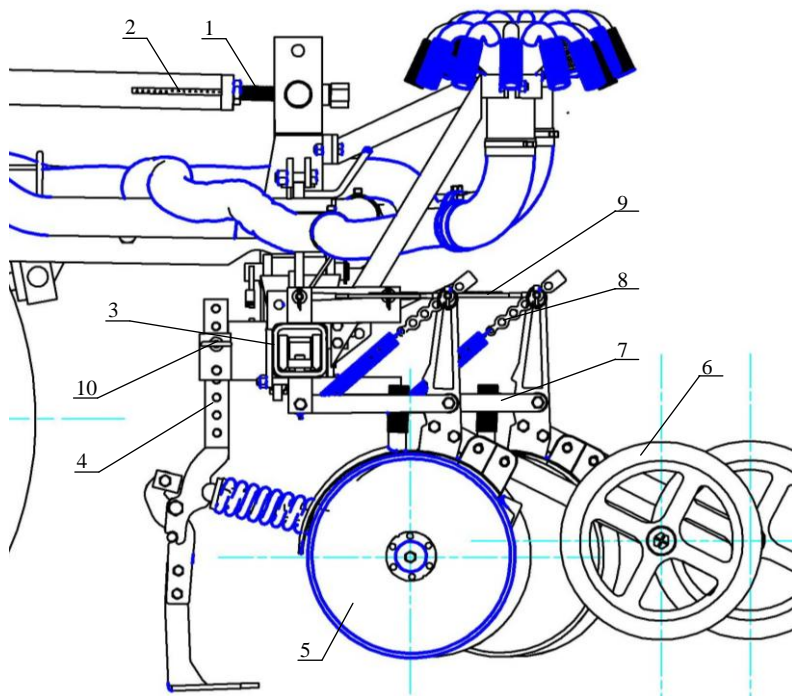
Механизм регулировки глубины заделки семян: 1 – регулировочный винт; 2 – шкала; 3 – сошниковый брус; 4 – следорыхлитель; 5 – сошник; 6 – прикатывающее колесо; 7 – нижний рычаг; 8 – устройство регулирования натяжения пружин; 9 – верхний рычаг; 10 – регулировочный штифт следорыхлителя.
